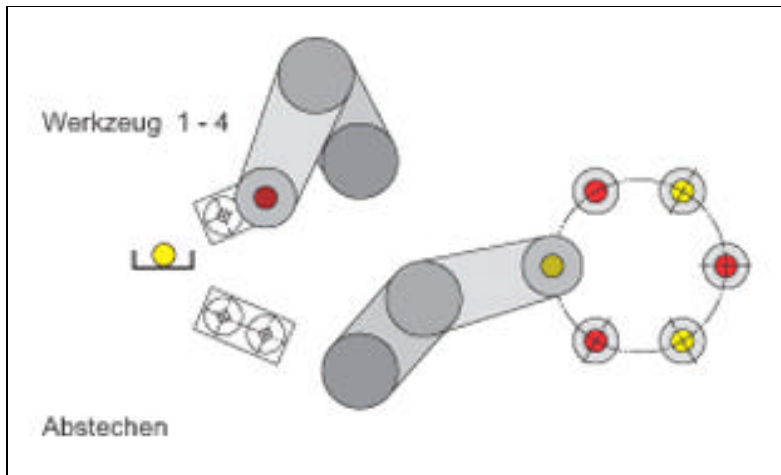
Takthalbierung der Rückseitenbearbeitung mit 2 Scara-Synchronspindeln
